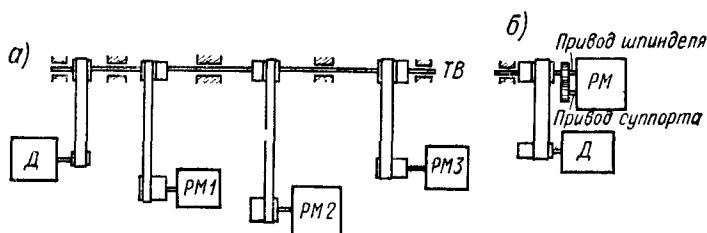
Схемы приводов: а — групповой привод; б — одиночный привод
